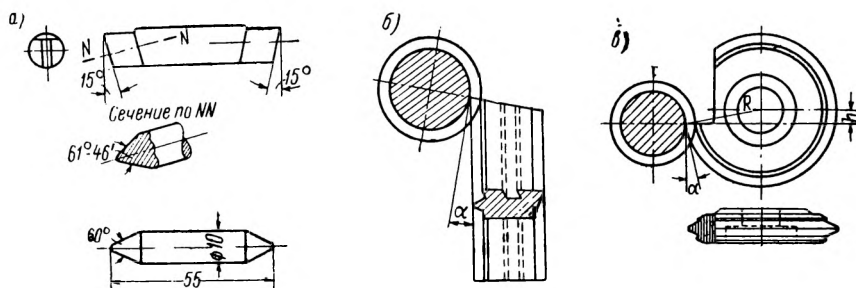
Типы резьбовых резцов: а — стержневой; б — призматический; в — дисковый.
